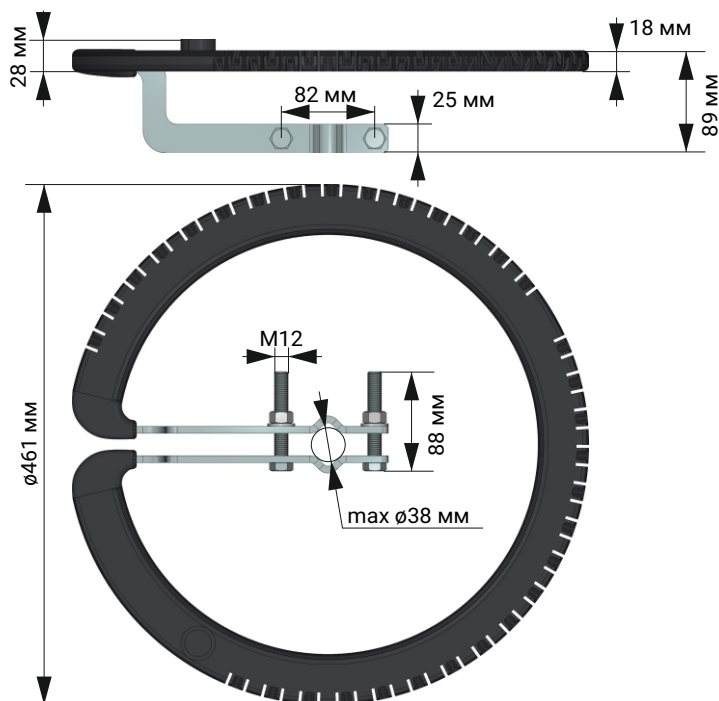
Габаритные и присоединительные размеры разрядного элемента
